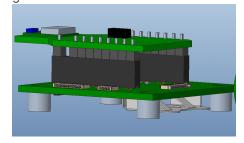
Elektronik- und Sensorikkomponenten im Werkzeug (Entwurf)
